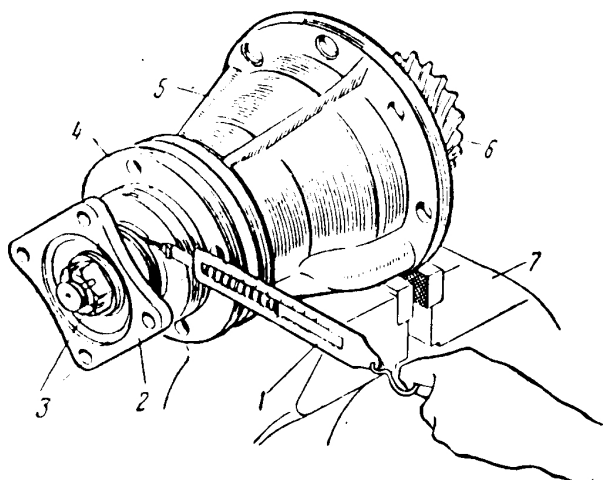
Проверка затяжки подшипников вала ведущей конической шестерни автомобиля ЗИЛ-130:
